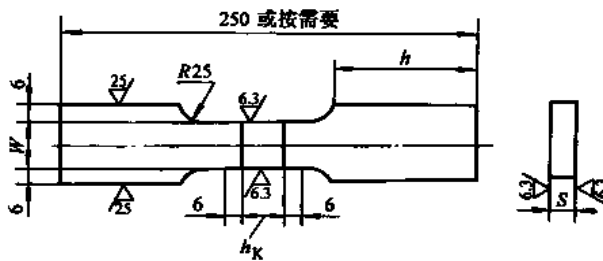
板材焊接接头拉伸试样形式及尺寸
